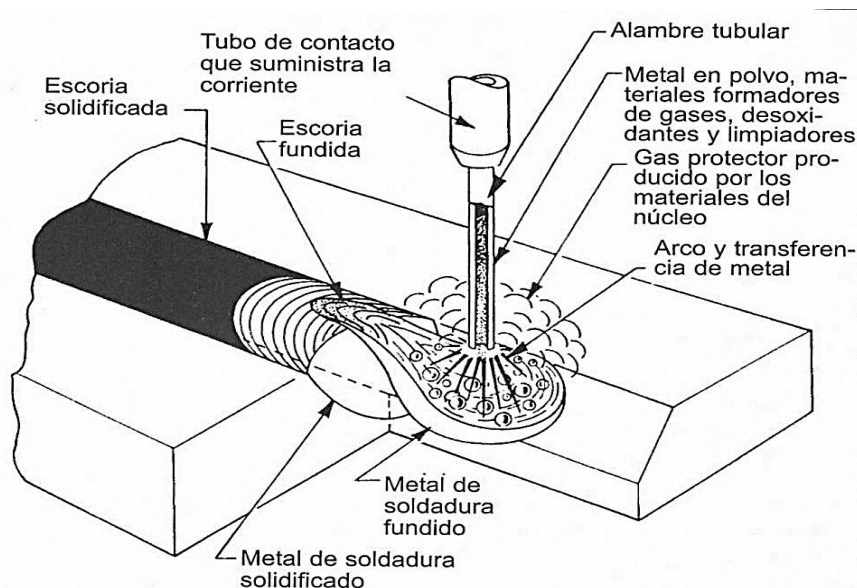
Proceso de soldadura con alambre tubular con protección gaseosa
